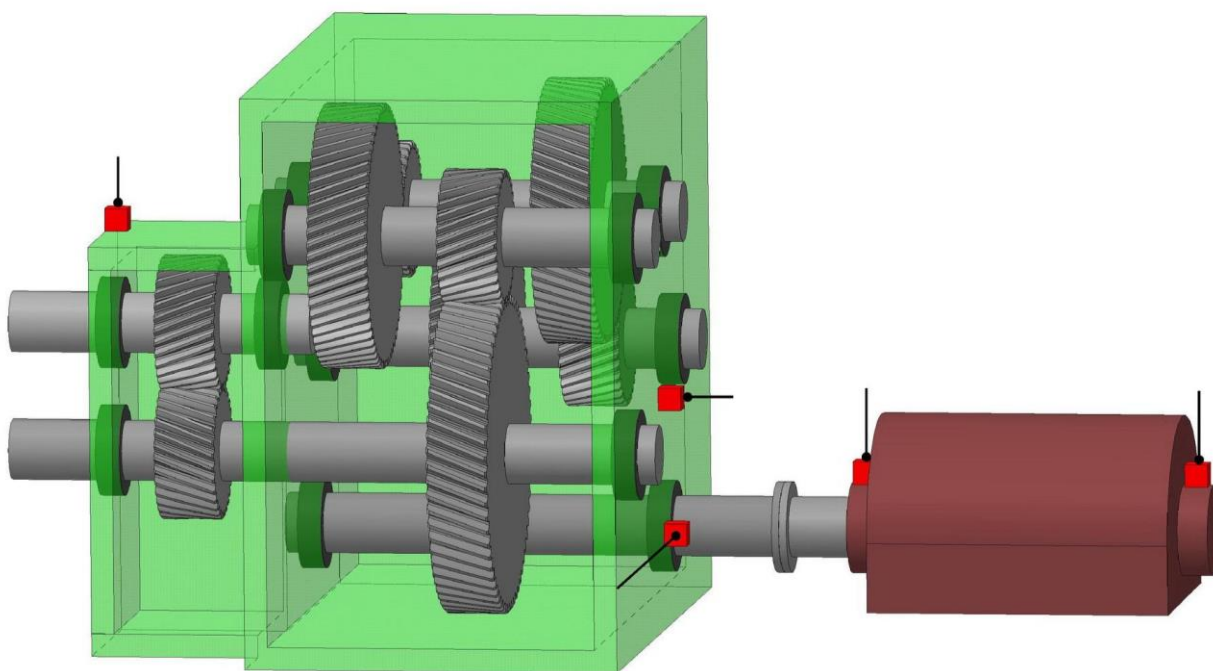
Расположение датчиков вибрации на двигателе и редукторе привода прокатной клетки
